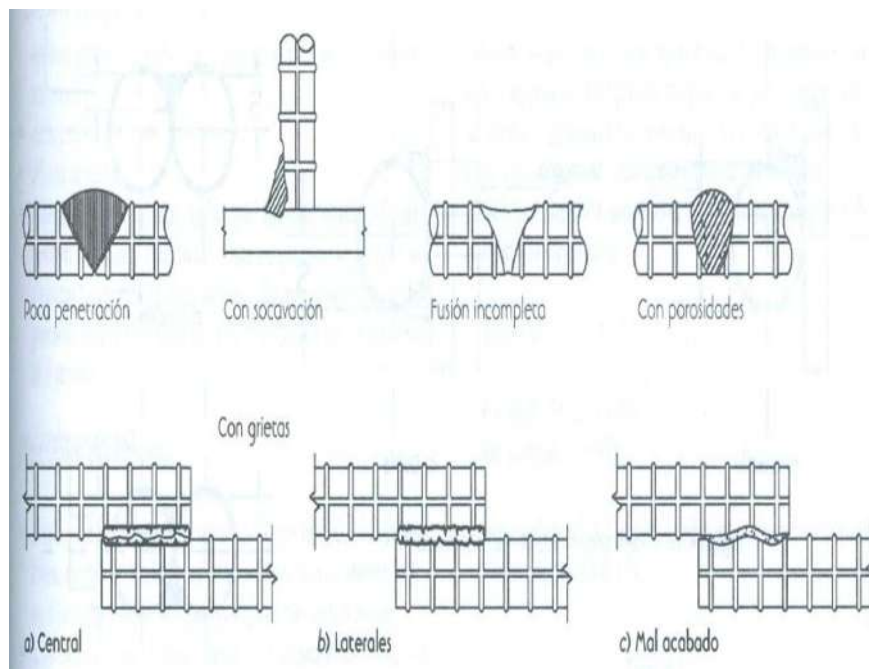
IMAGEN VI – CARACTERISITCAS DE LA SOLDADURA
